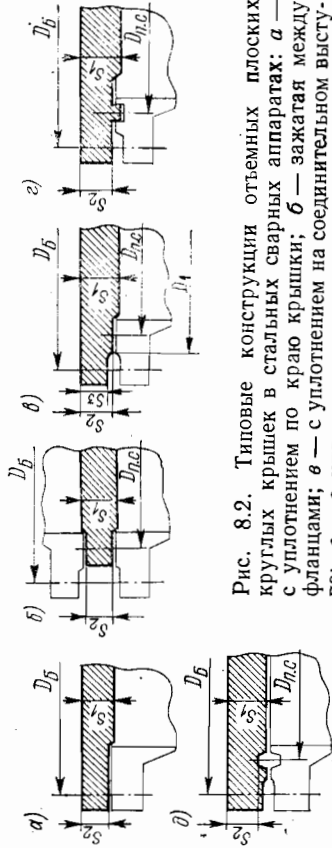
Типовые конструкции отъемных плоских круглых крышек в стальных сварных аппаратах: а — с уплотнением по краю крышки; б — зажатая между фланцами; в — с уплотнением на соединительном выступе; г — с уплотнением выступ — впадина или шип — паз; д — с уплотнением овальной или восьмиугольной прокладкой
